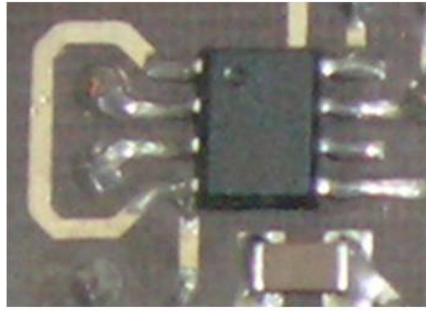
Yüzey montaj OPA129 için sızıntı akımı engelleme tekniği.
